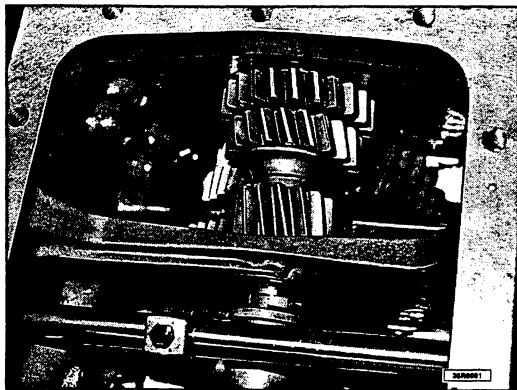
Engranajes de la T.D.F. trasera - 4 velocidades para Explorer II.
